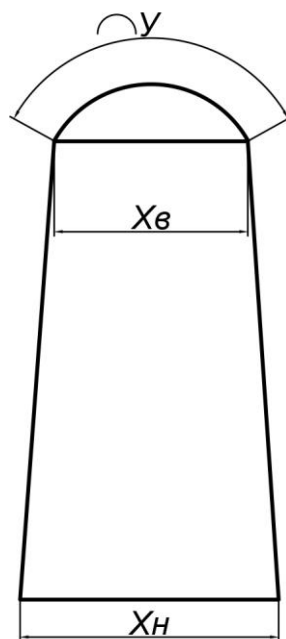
Обозначения размеров сумки, закрывающейся на клапан для определения размеров шпации
